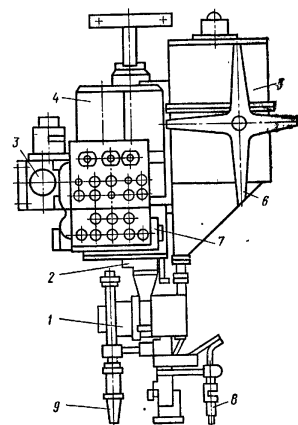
Базовый унифицированный сварочный автомат А-1401:
